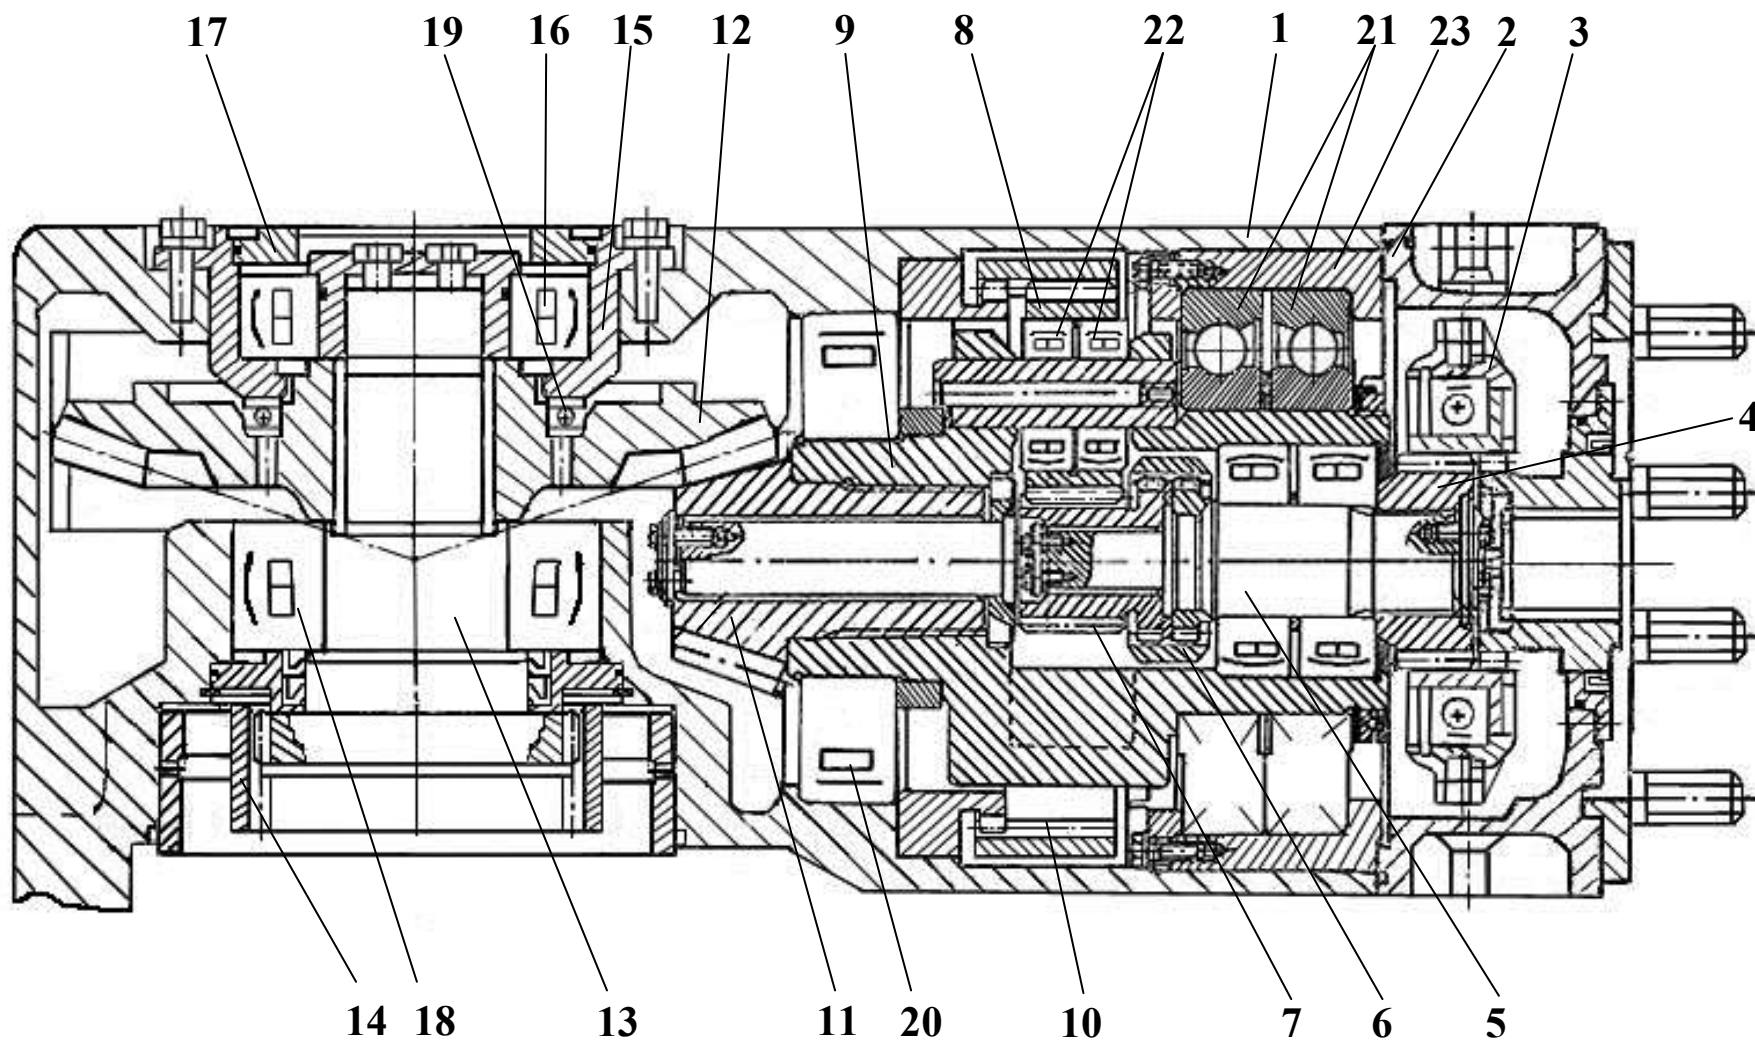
Редуктор центральный привода правого исполнительного органа
